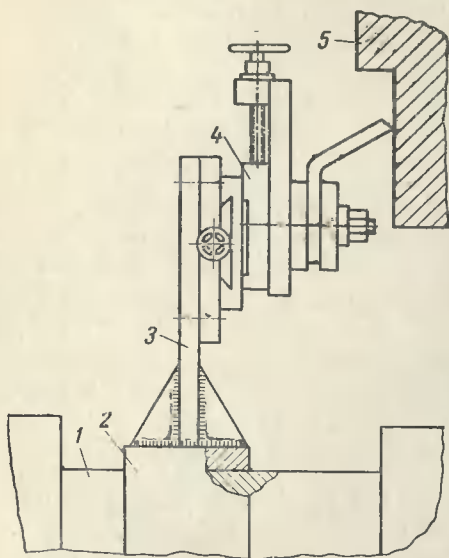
Приспособление для проточки торцевой поверхности наружного щита.
